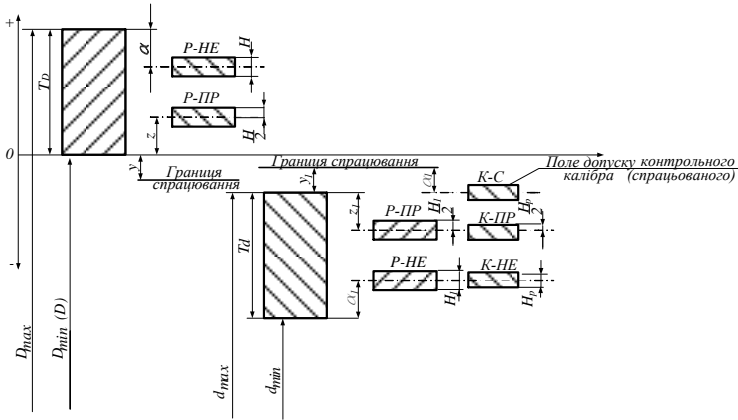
Схема розташування полів допусків робочих і контрольних калібрів
